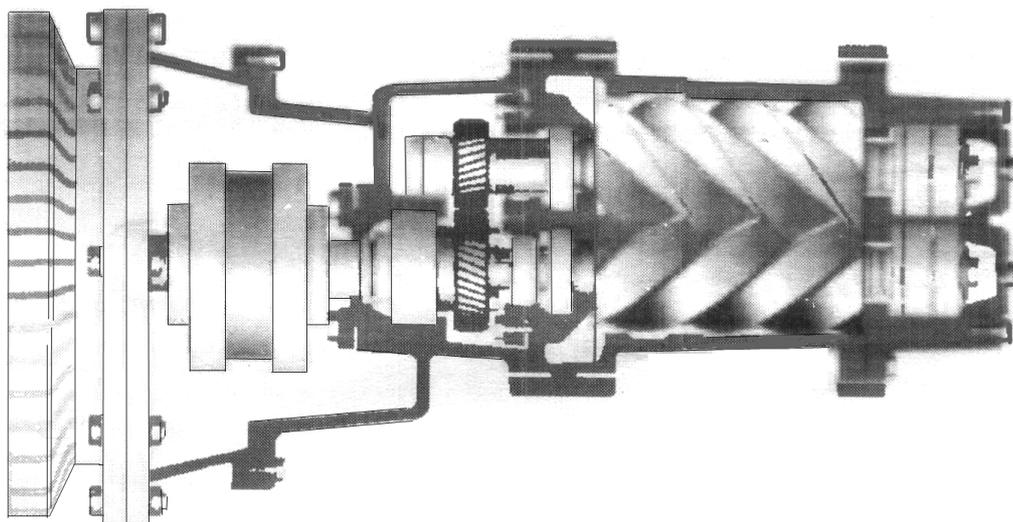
Маслосмазываемый винтовой компрессор
